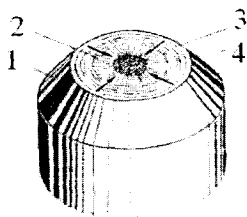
Схема будови поверхні злому за розтягування циліндричного зразка з проточкою:
